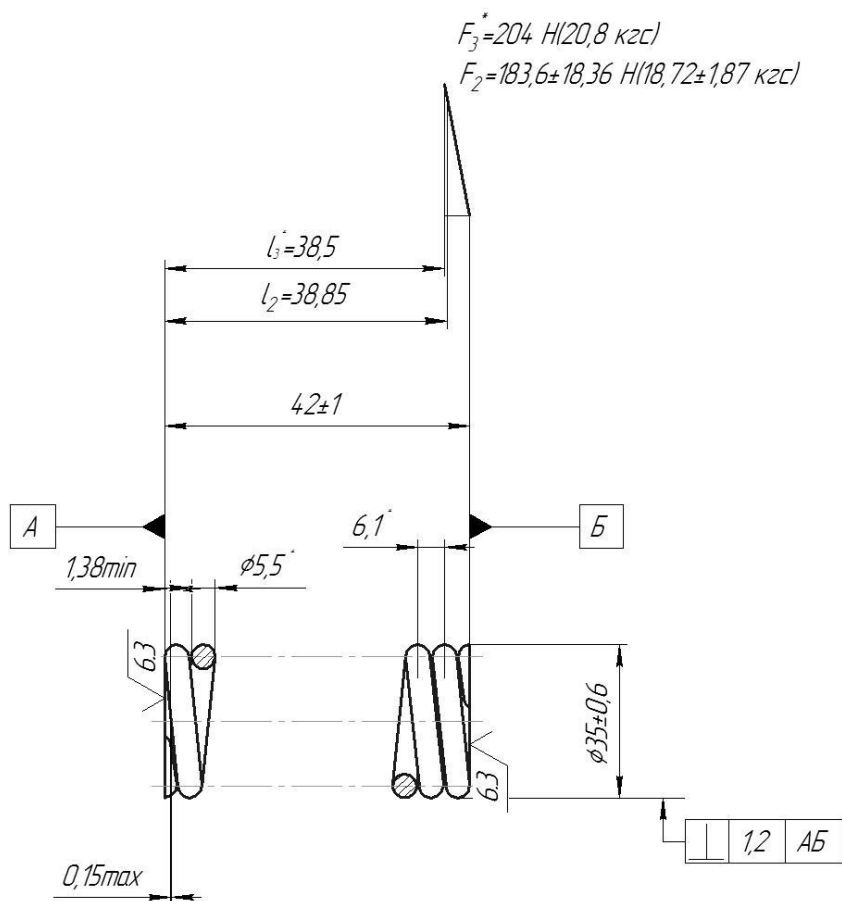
Эскиз пружины сжатия главного цилиндра
